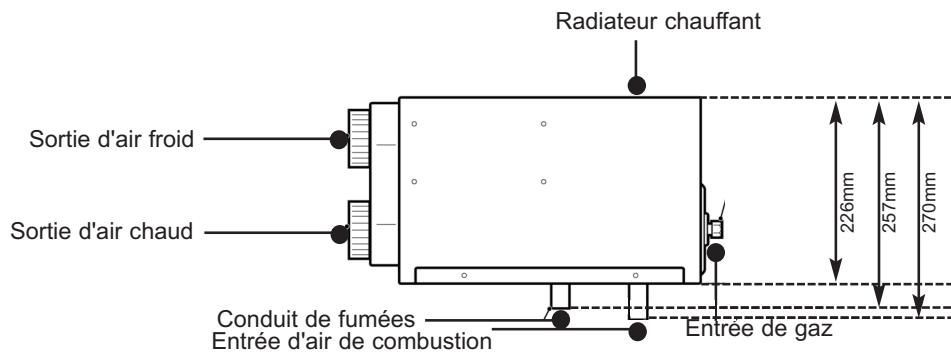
Installation interne - Vue latérale - SH2202 ou SC2202
